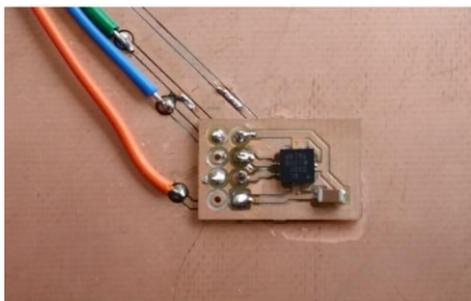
Detalle de la placa de circuito impresa diseñada para caracterizar el acelerómetro.
